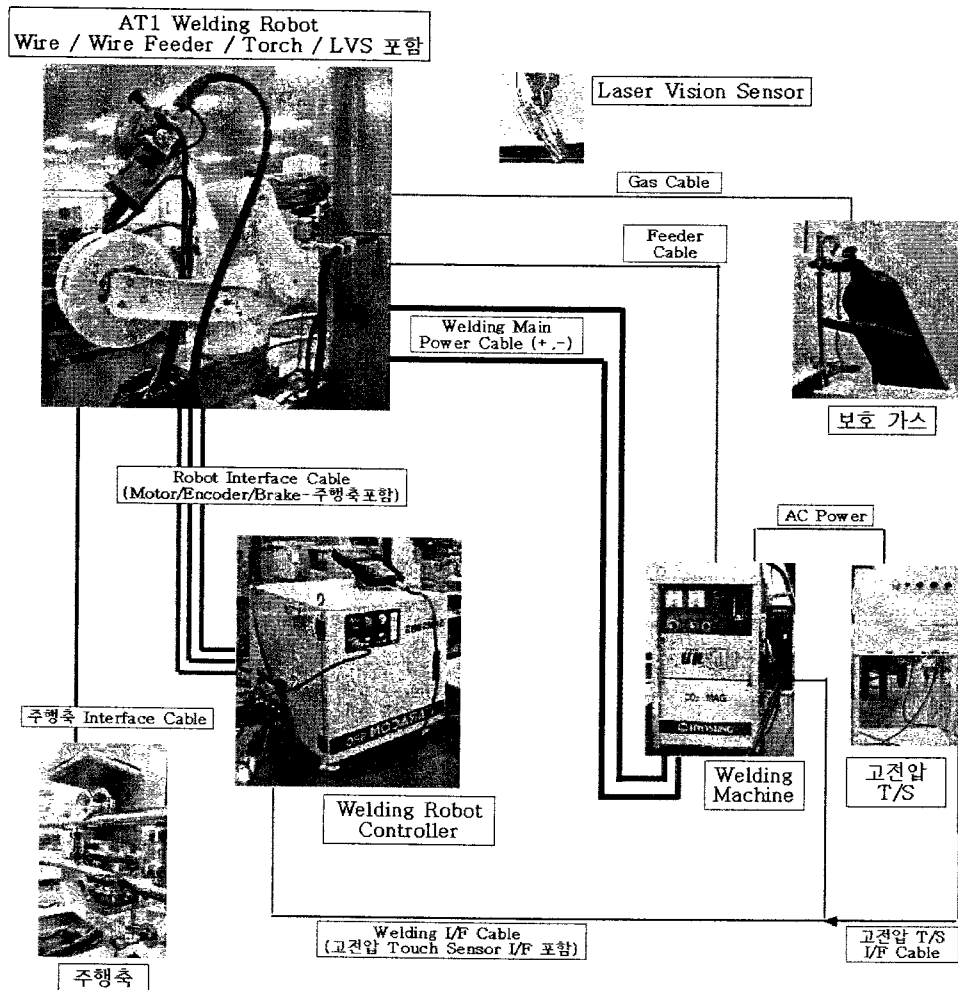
수직철골 용접 시스템의 System layout
